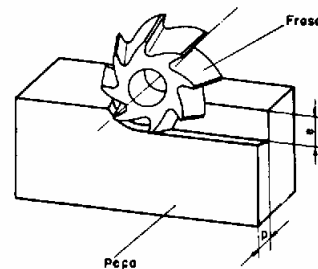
Fresamento frontal. Profundidade de corte a_p ; espessura de penetração e .
